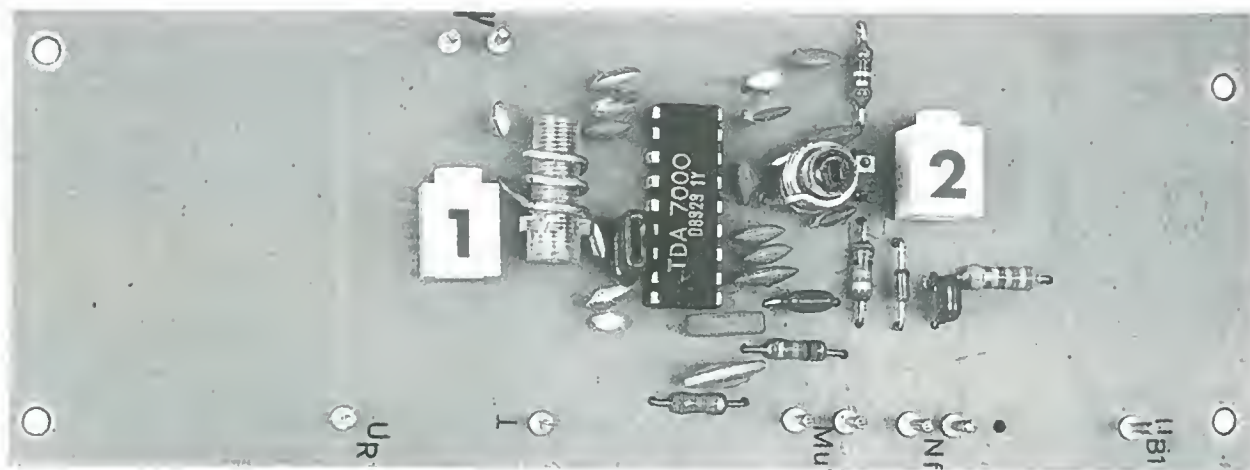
La basetta del ricevitore FM dovrà avere piccole dimensioni, con un montaggio molto raccolto dei componenti: le dimensioni sono 52 x 135 mm.
